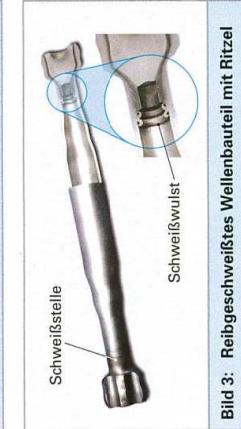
Reibgeschweißtes Wellenbauteil mit Ritzel
